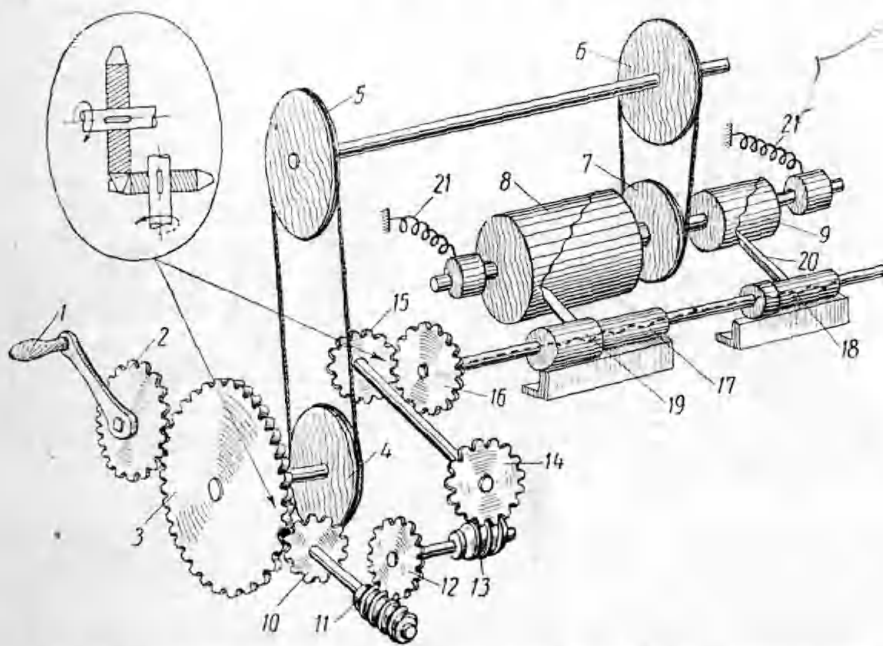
Большой токарно-копировальный станок Нартова 1718—1729 гг.
